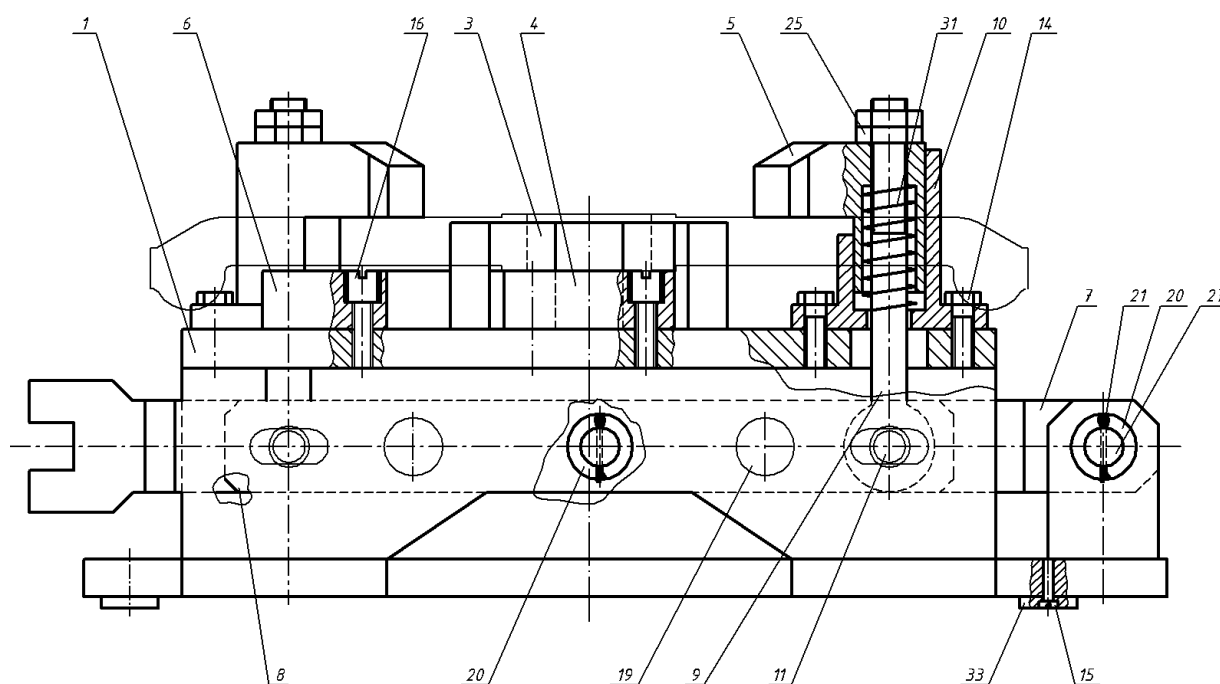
Пристрій для фрезерування деталі 65-20027 в розмір 32
